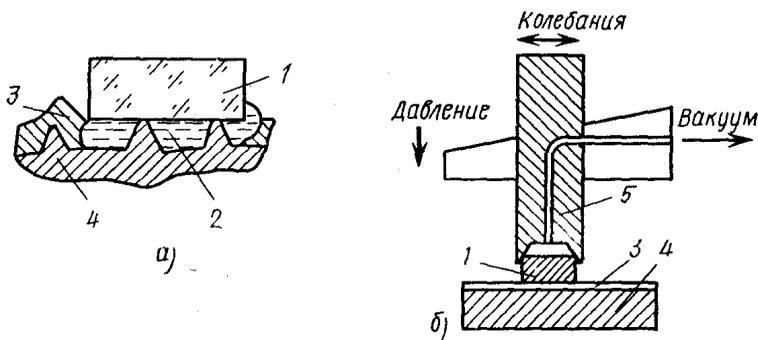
Схема соединения полупроводникового кристалла с основанием керамического корпуса:
